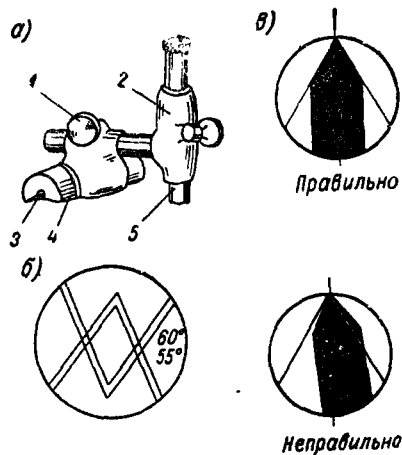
Установка резьбового резца с помощью специальной лупы.
